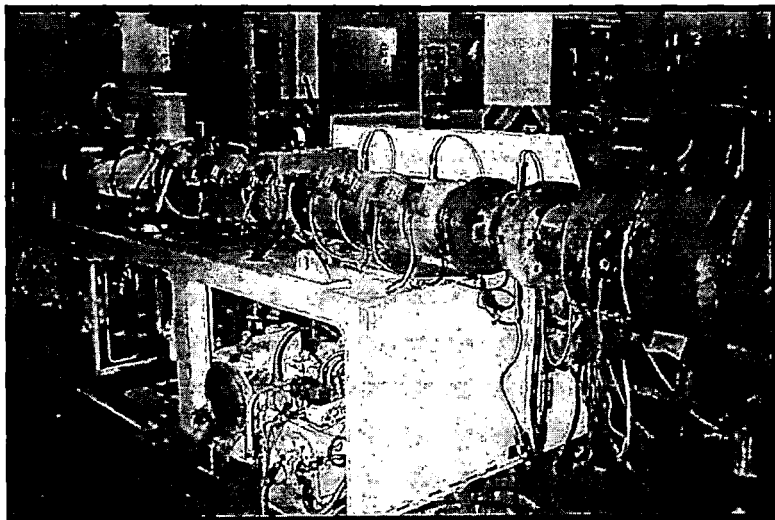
Foto conjunto barril – Tornillos. Línea 3
